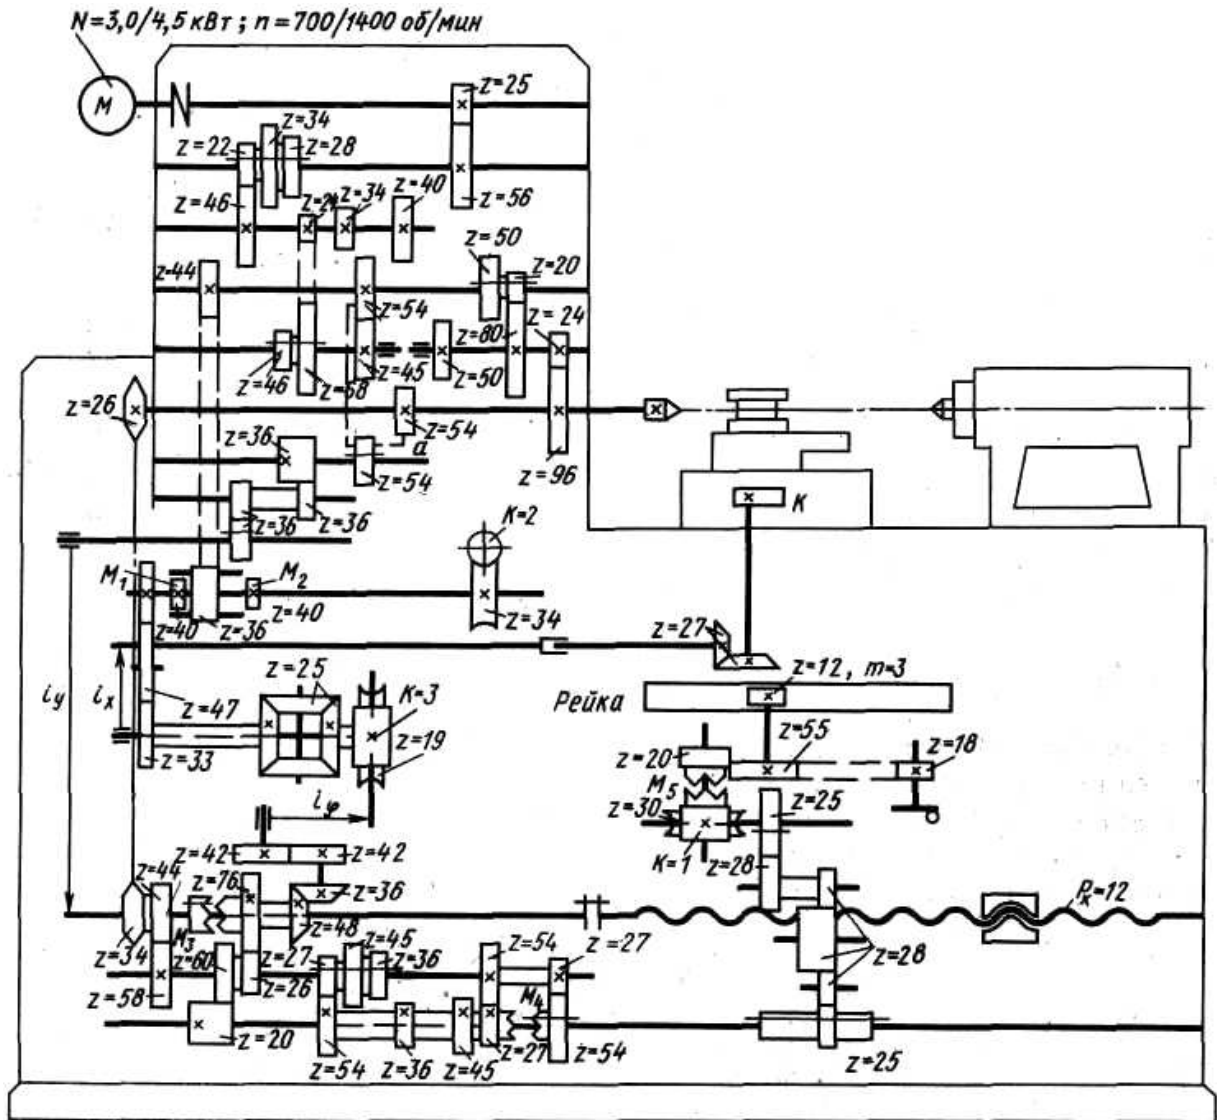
Кинематическая схема токарно-затыловочного станка
